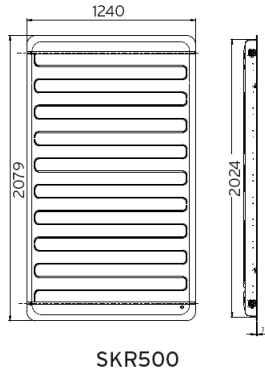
Dibujo técnico del captador SKR500 con dimensiones
